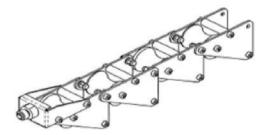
Rodillos de cable para fondo de pozo (MK2).
